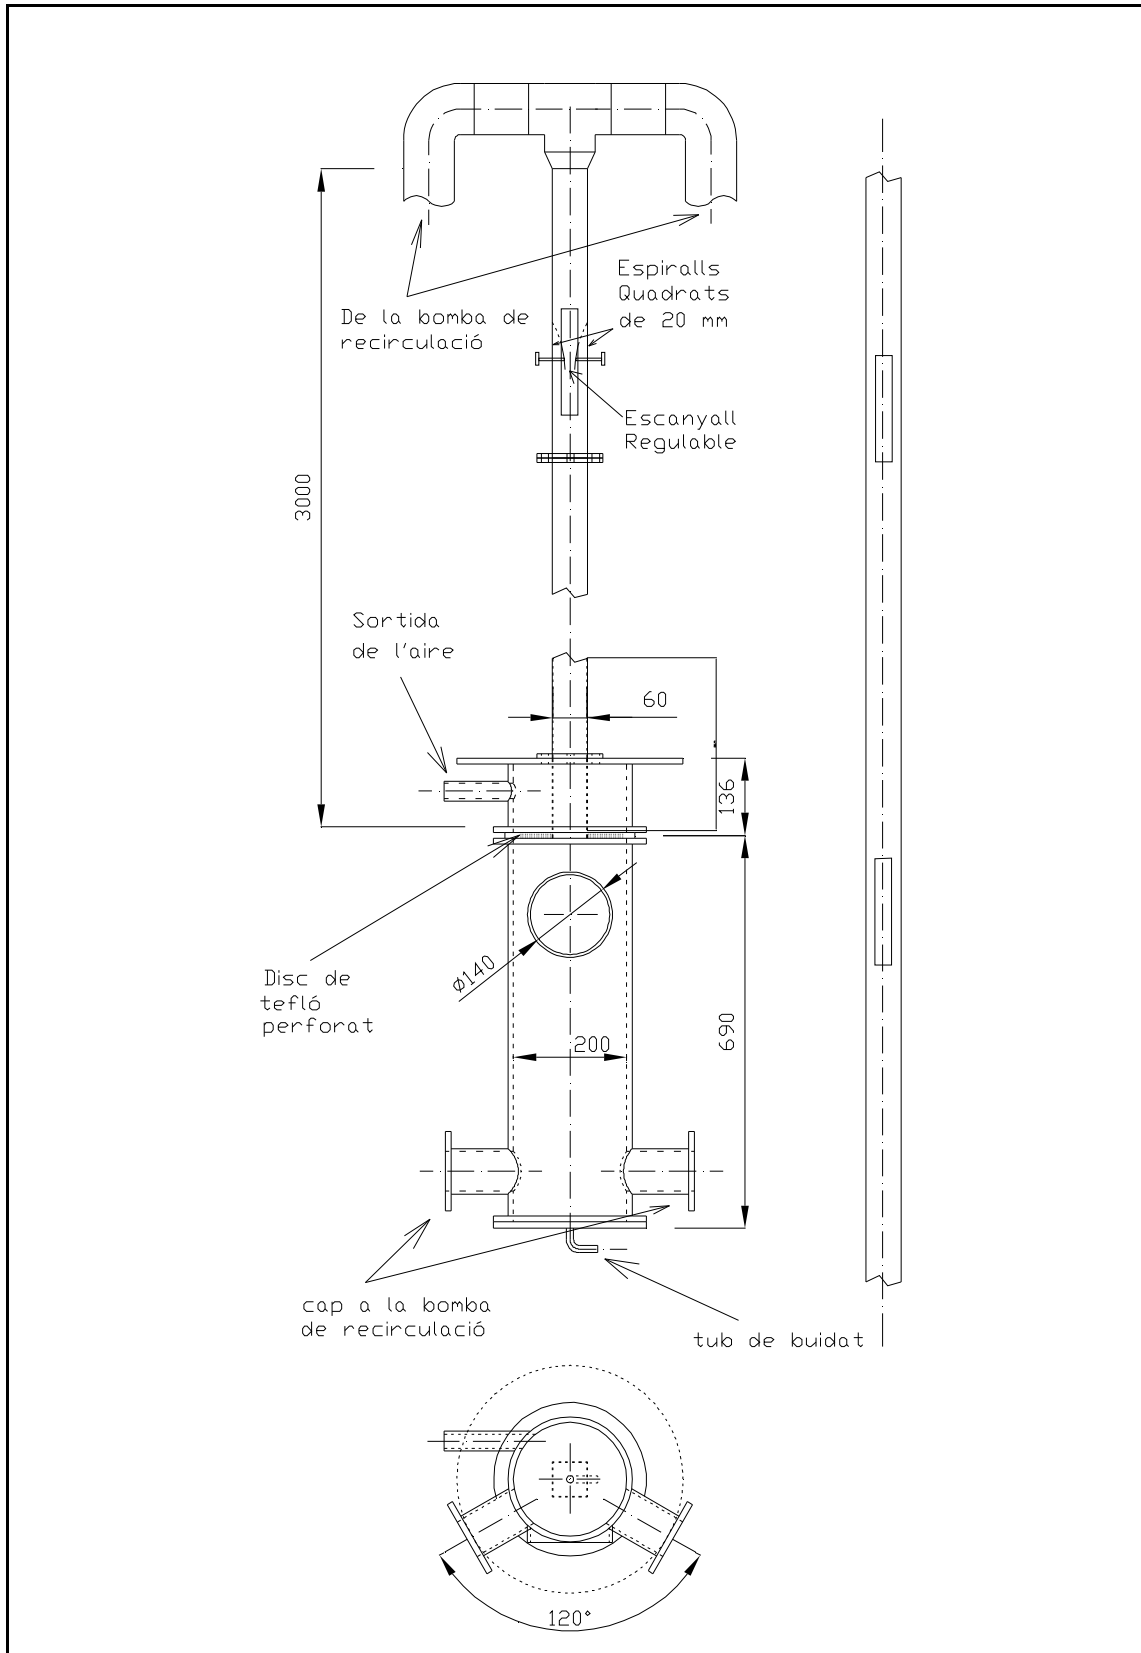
Croquis amb les principals dimensions i elements de la trompa d'aigua construïda
